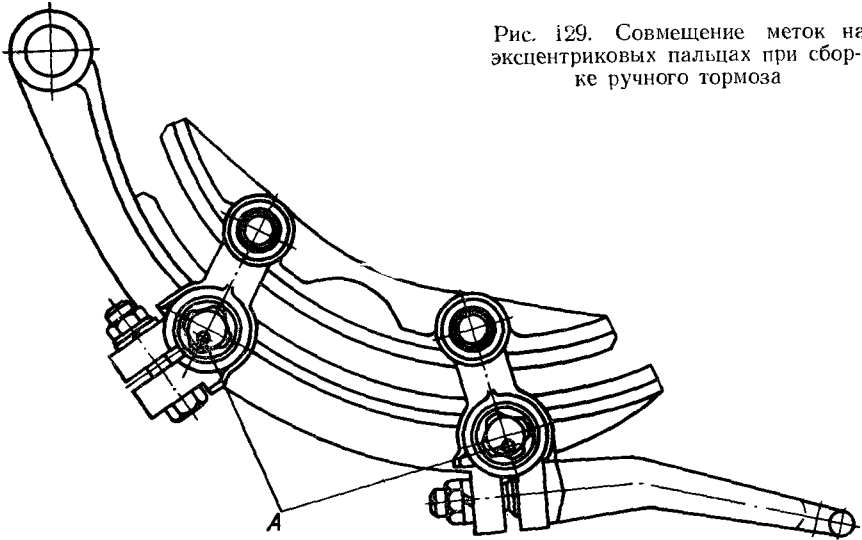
Совмещение меток на эксцентриковых пальцах при сборке ручного тормоза
